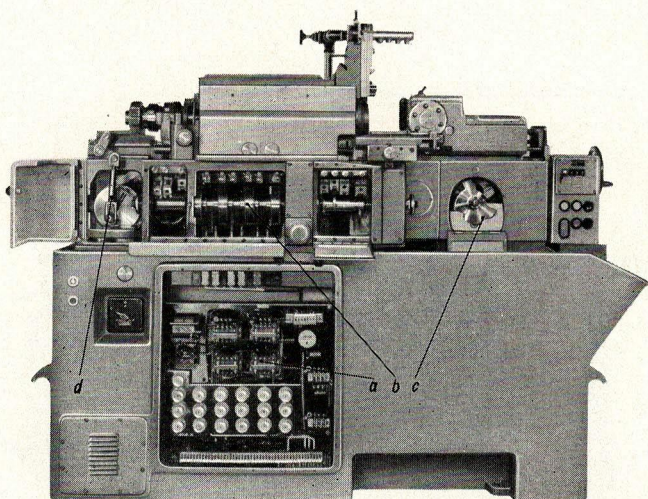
Maschinenvorderseite. Schaltgeräte und Steuerwellenraum geöffnet
